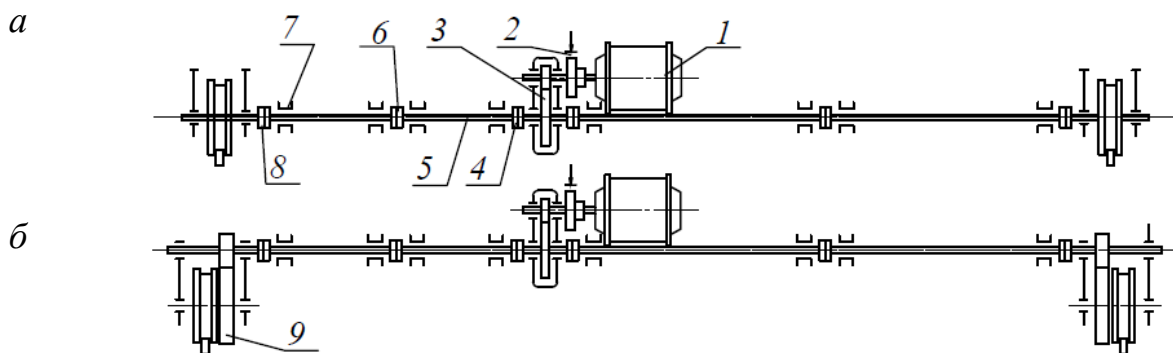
Механизм передвижения с тихоходным трансмиссионным валом: а – без открытой зубчатой передачи; б – с открытой зубчатой передачей
